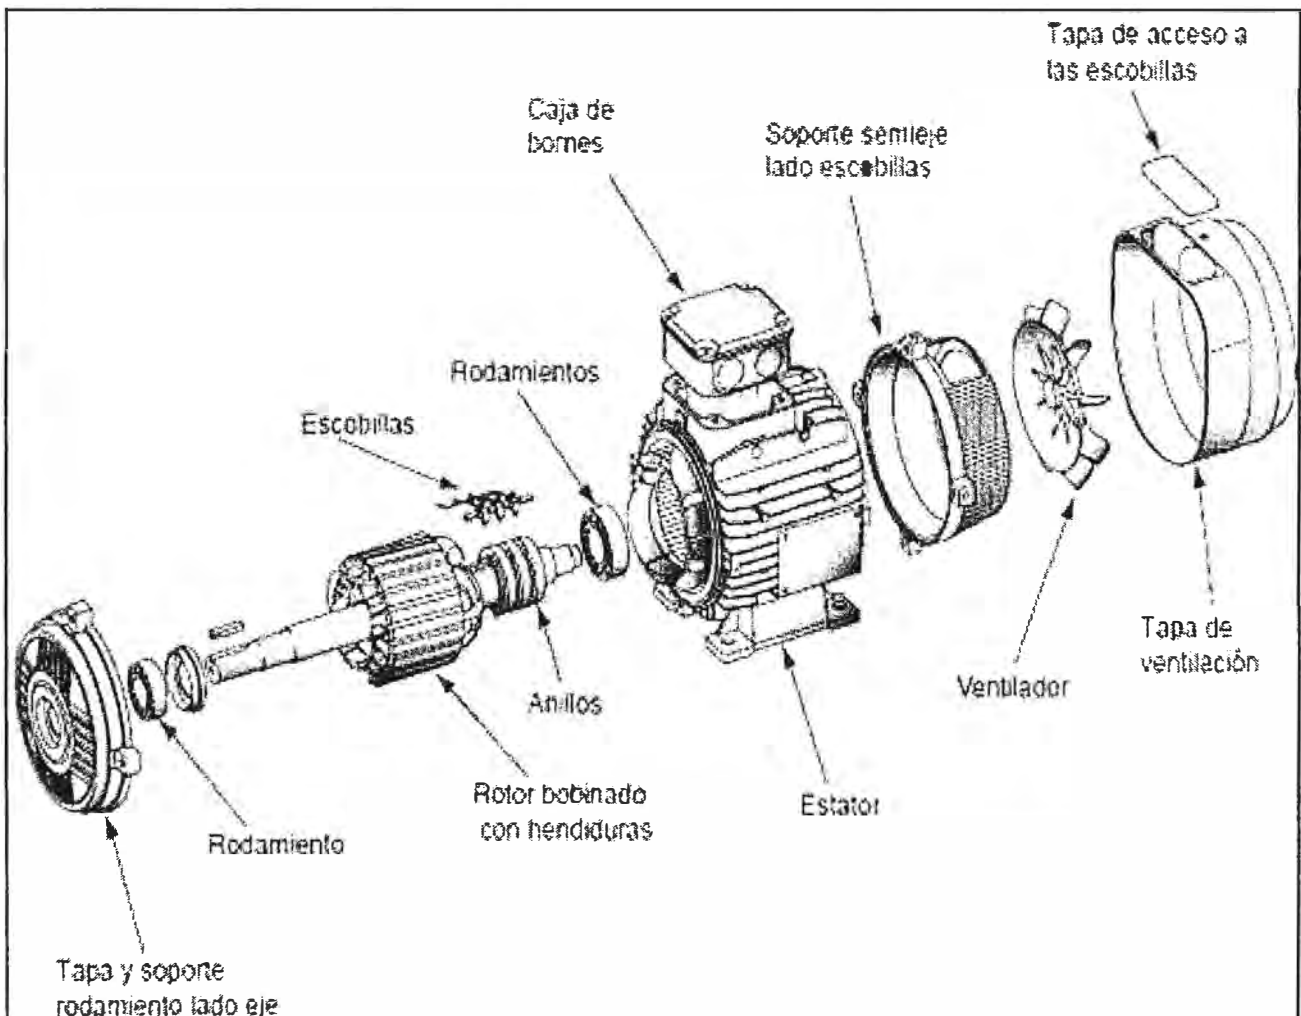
Partes de un Motor Asíncrono de Rotor Bobinado
